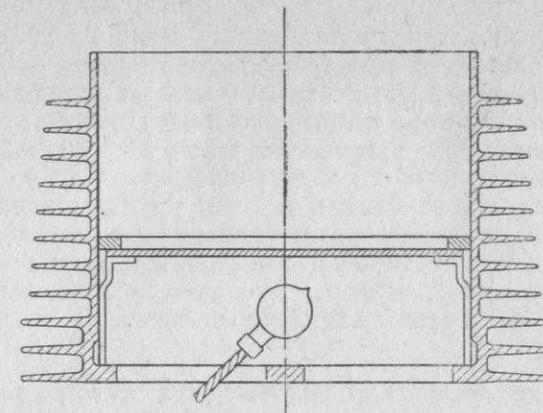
Приспособление для проверки поршневых колец на прилегание к стенкам цилиндра.
